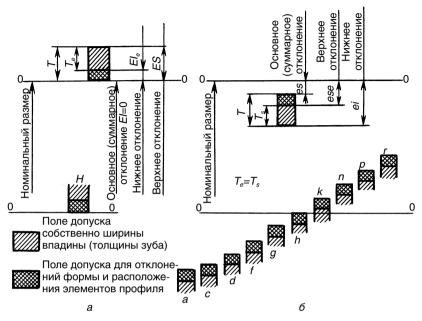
Расположение полей допусков для эвольвентных шлицевых соединений: а — ширины е впадины втулки; б — толщины зуба s
